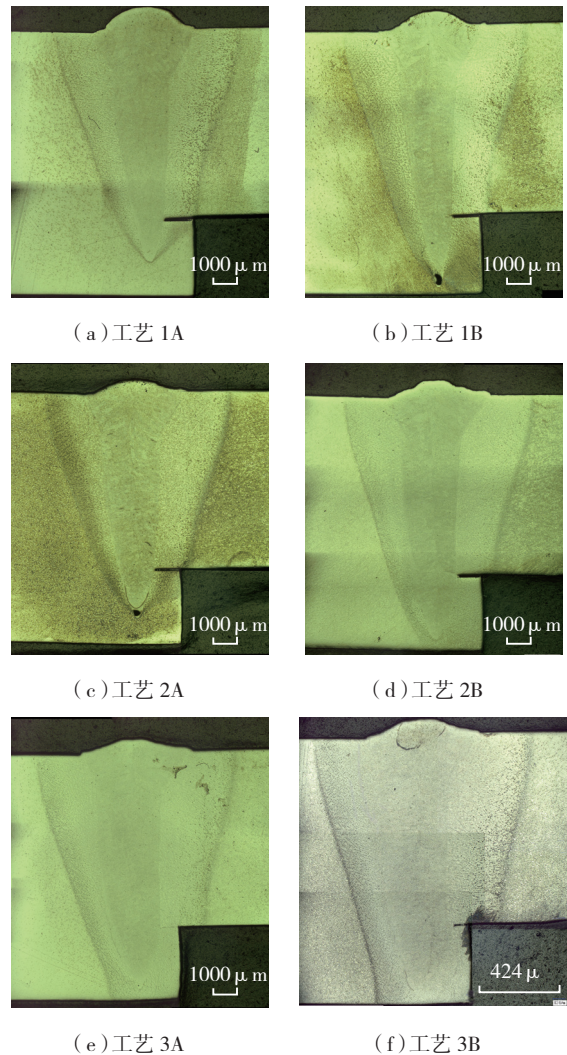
30CrMnSiNi2A 钢电子束焊缝横截面形貌
